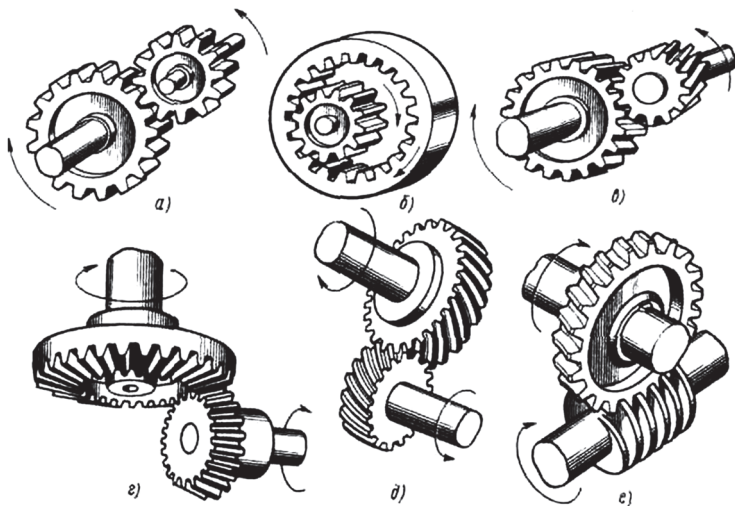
Зубчатые передачи (а-е) для вращательных движений
